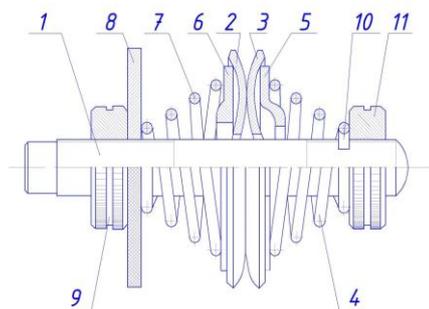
Конструктивная схема тарельчатого натяжителя игольной нити с двумя коническими пружинами
